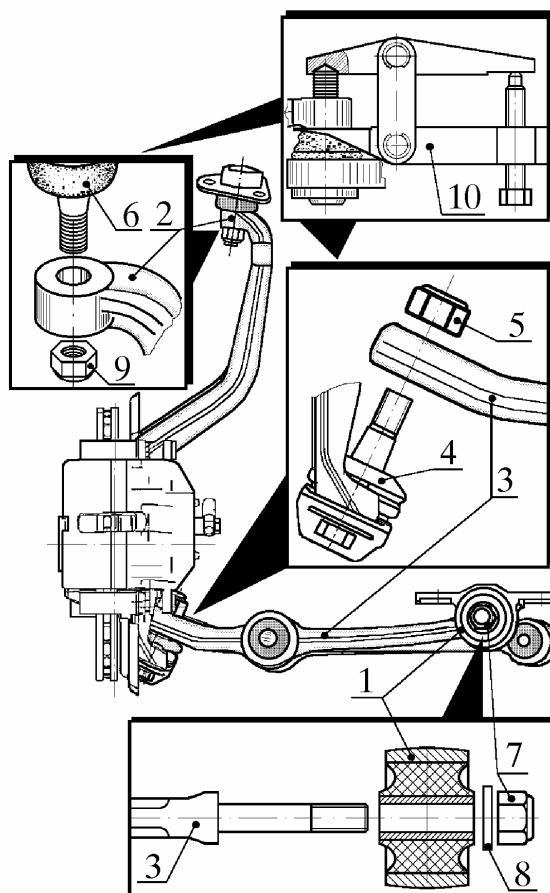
Снятие задней опоры, верхнего шарнира и нижнего рычага с сайлентблоком и шарниром амортизатора в сборе:
